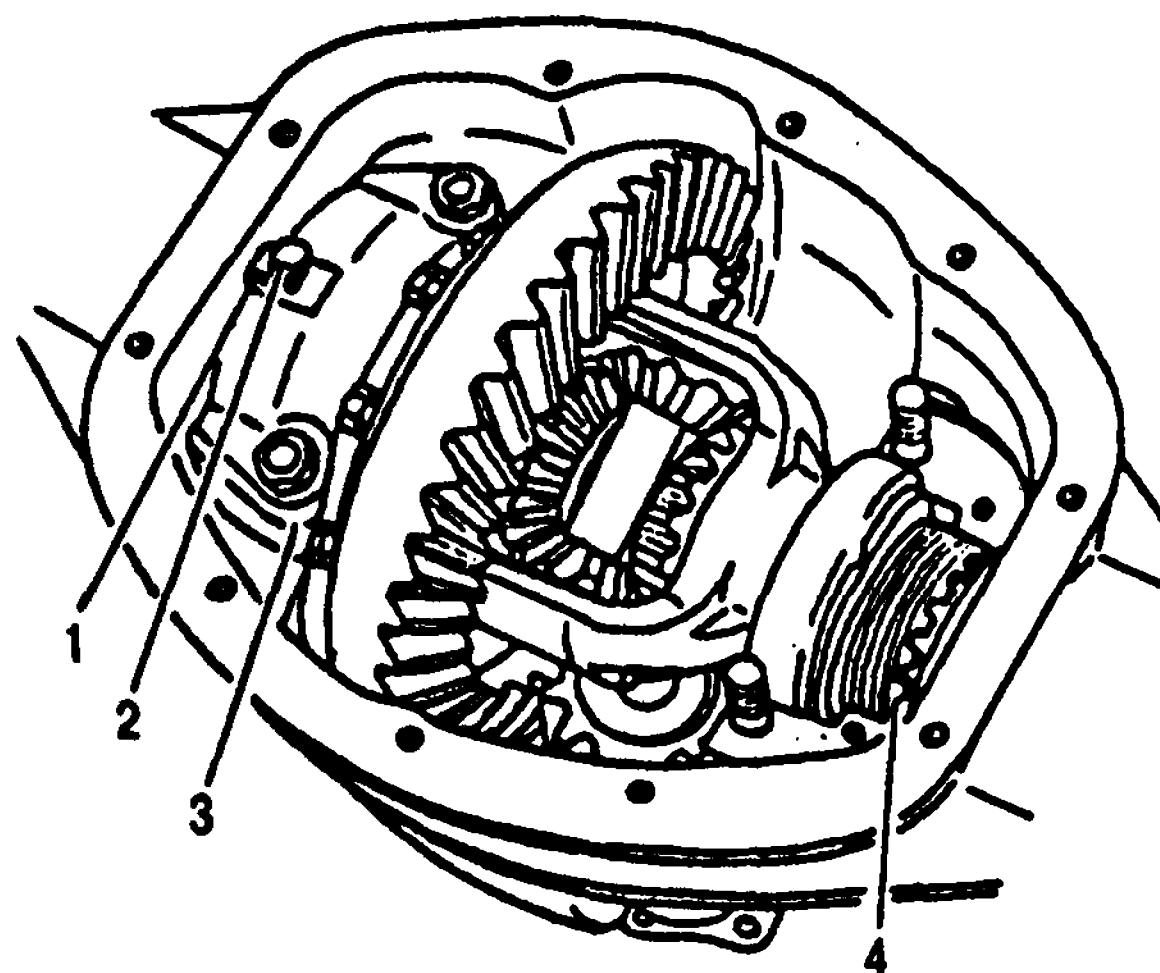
Установка дифференциала в картер заднего моста: 1 - стопорная пластина; 2 - болт крепления стопорной пластины; 3 - крышка подшипника дифференциала; 4 - регулировочная гайка подшипника дифференциала
